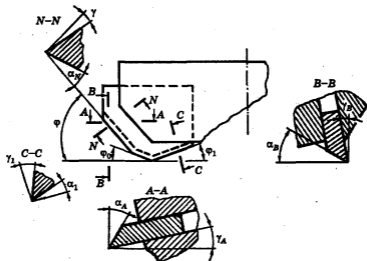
Геометрические параметры режущей части торцовой фрезы
